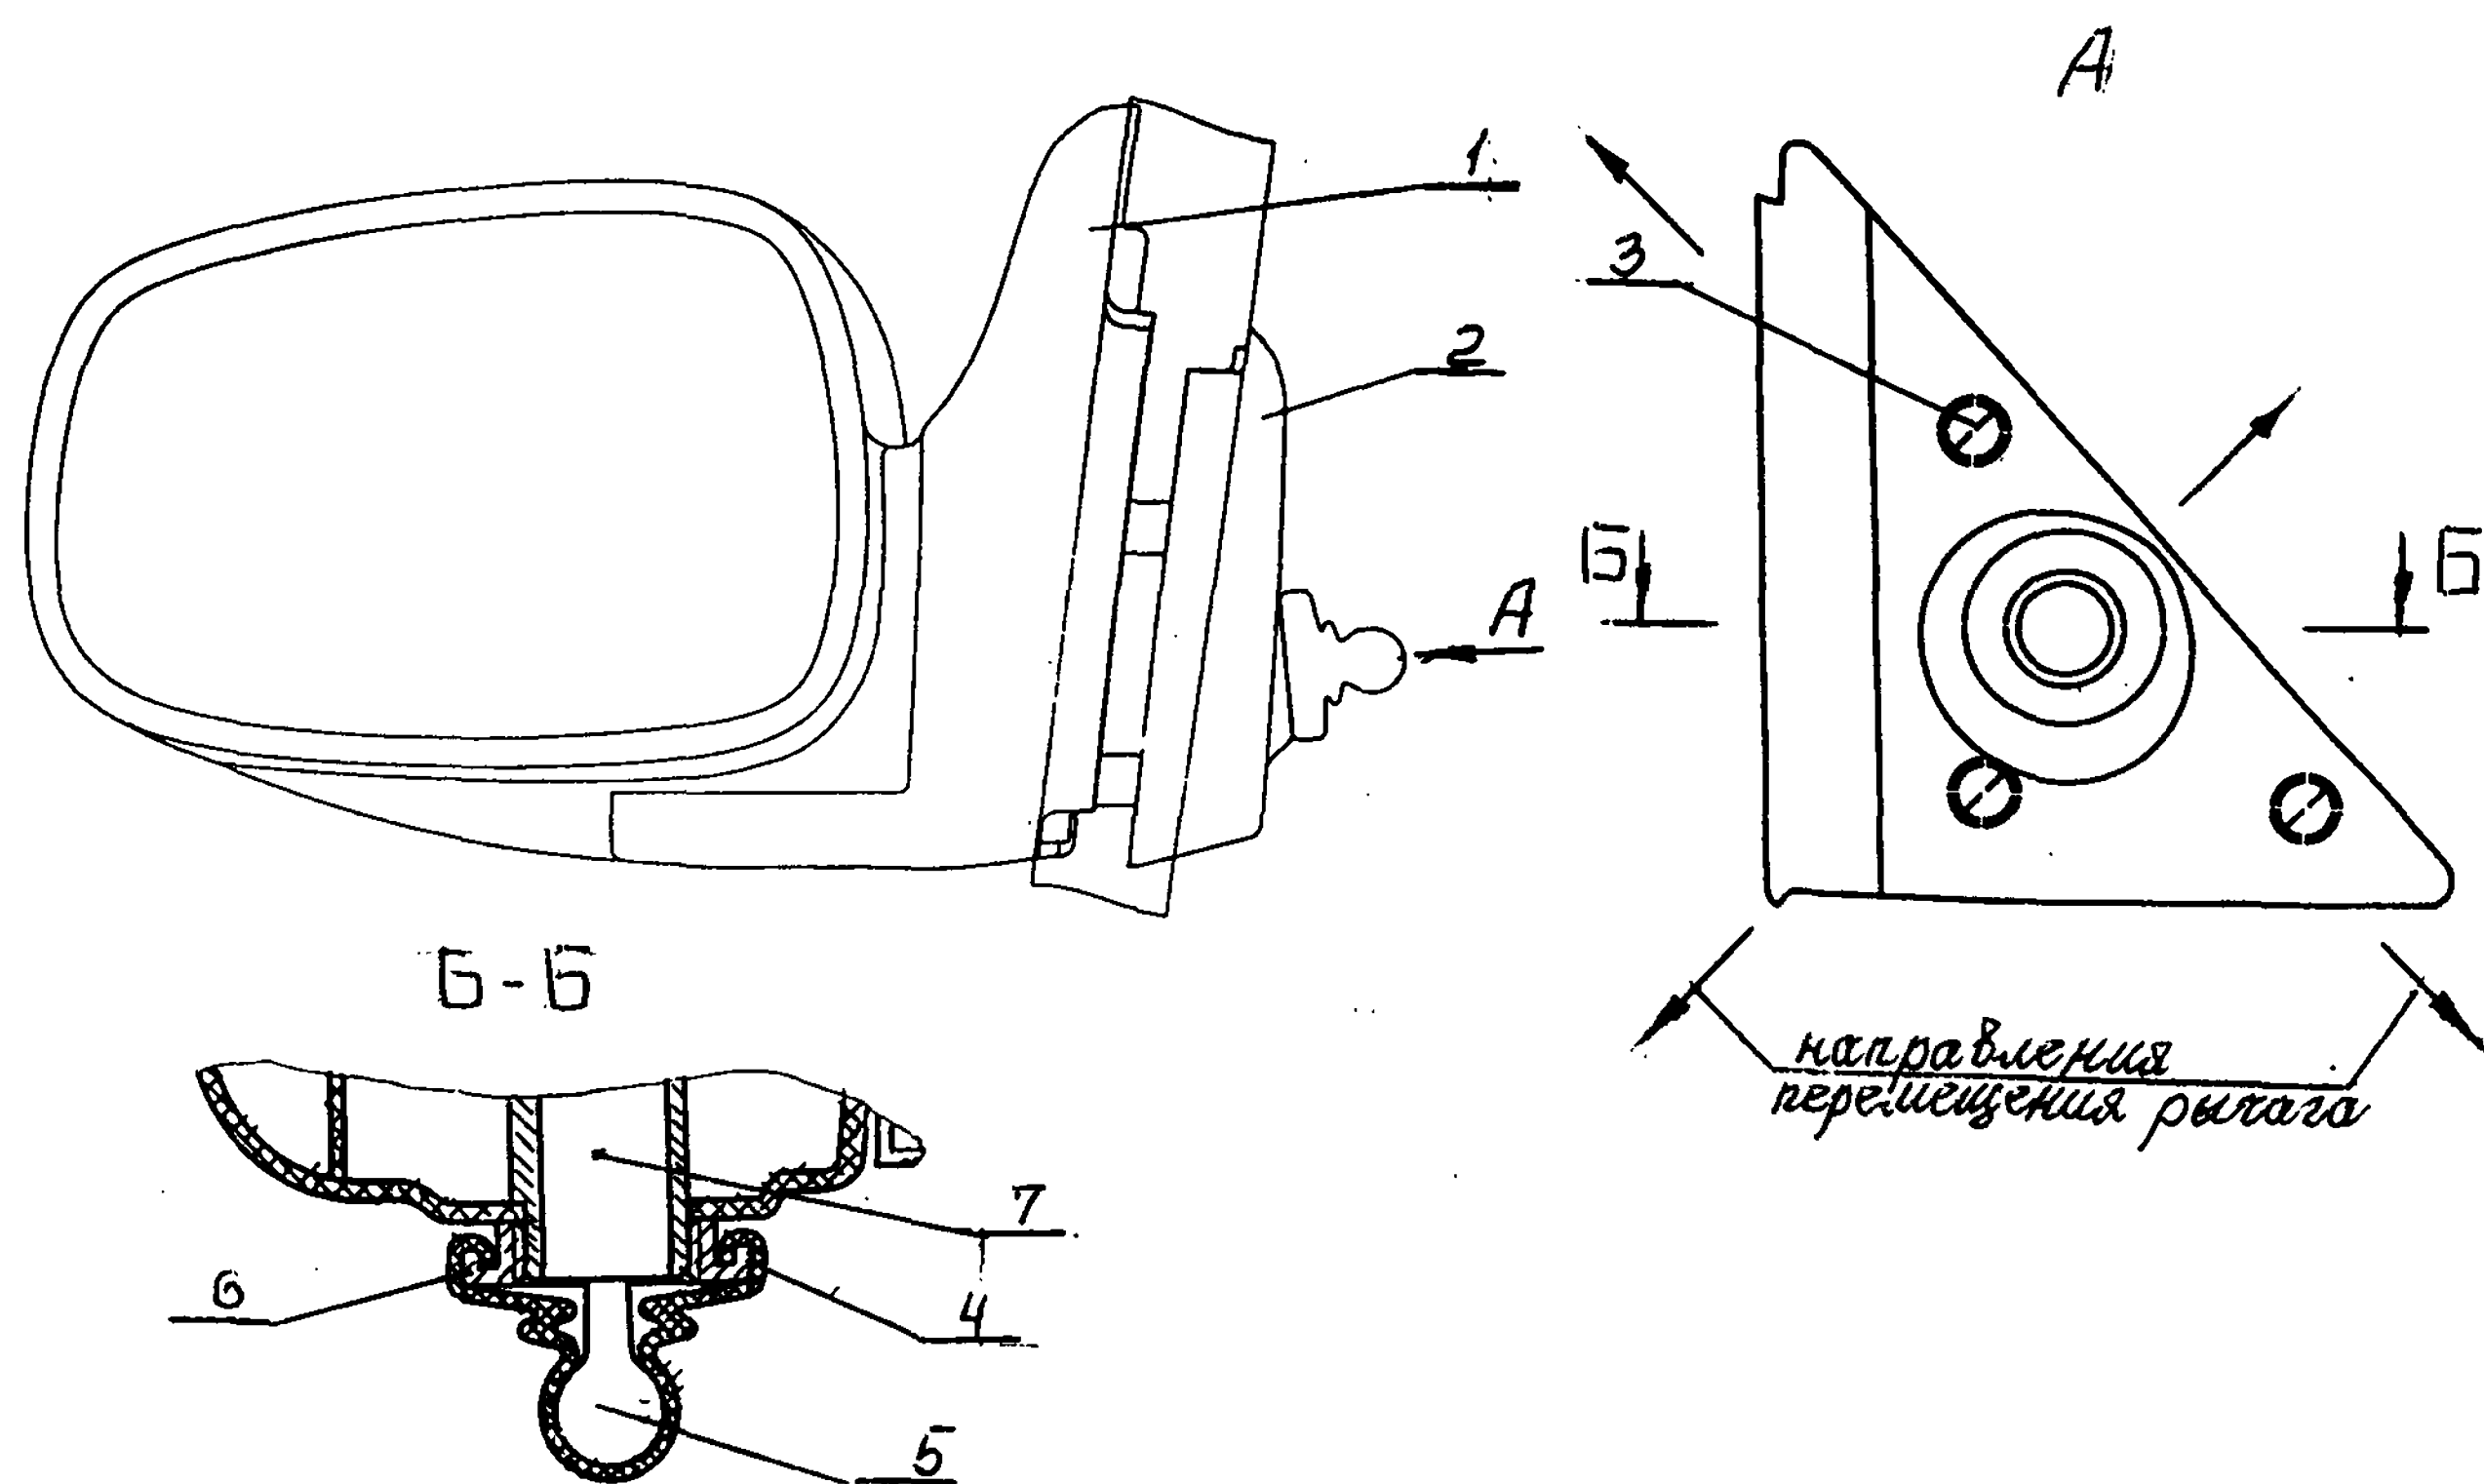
Зеркало заднего вида наружное: 1 - зеркало; 2 - опора зеркала; 3 - винт крепления зеркала; 4 - защитный чехол; 5 - рычаг управления зеркалом; 6 - гайка; 7 - пульт управления
